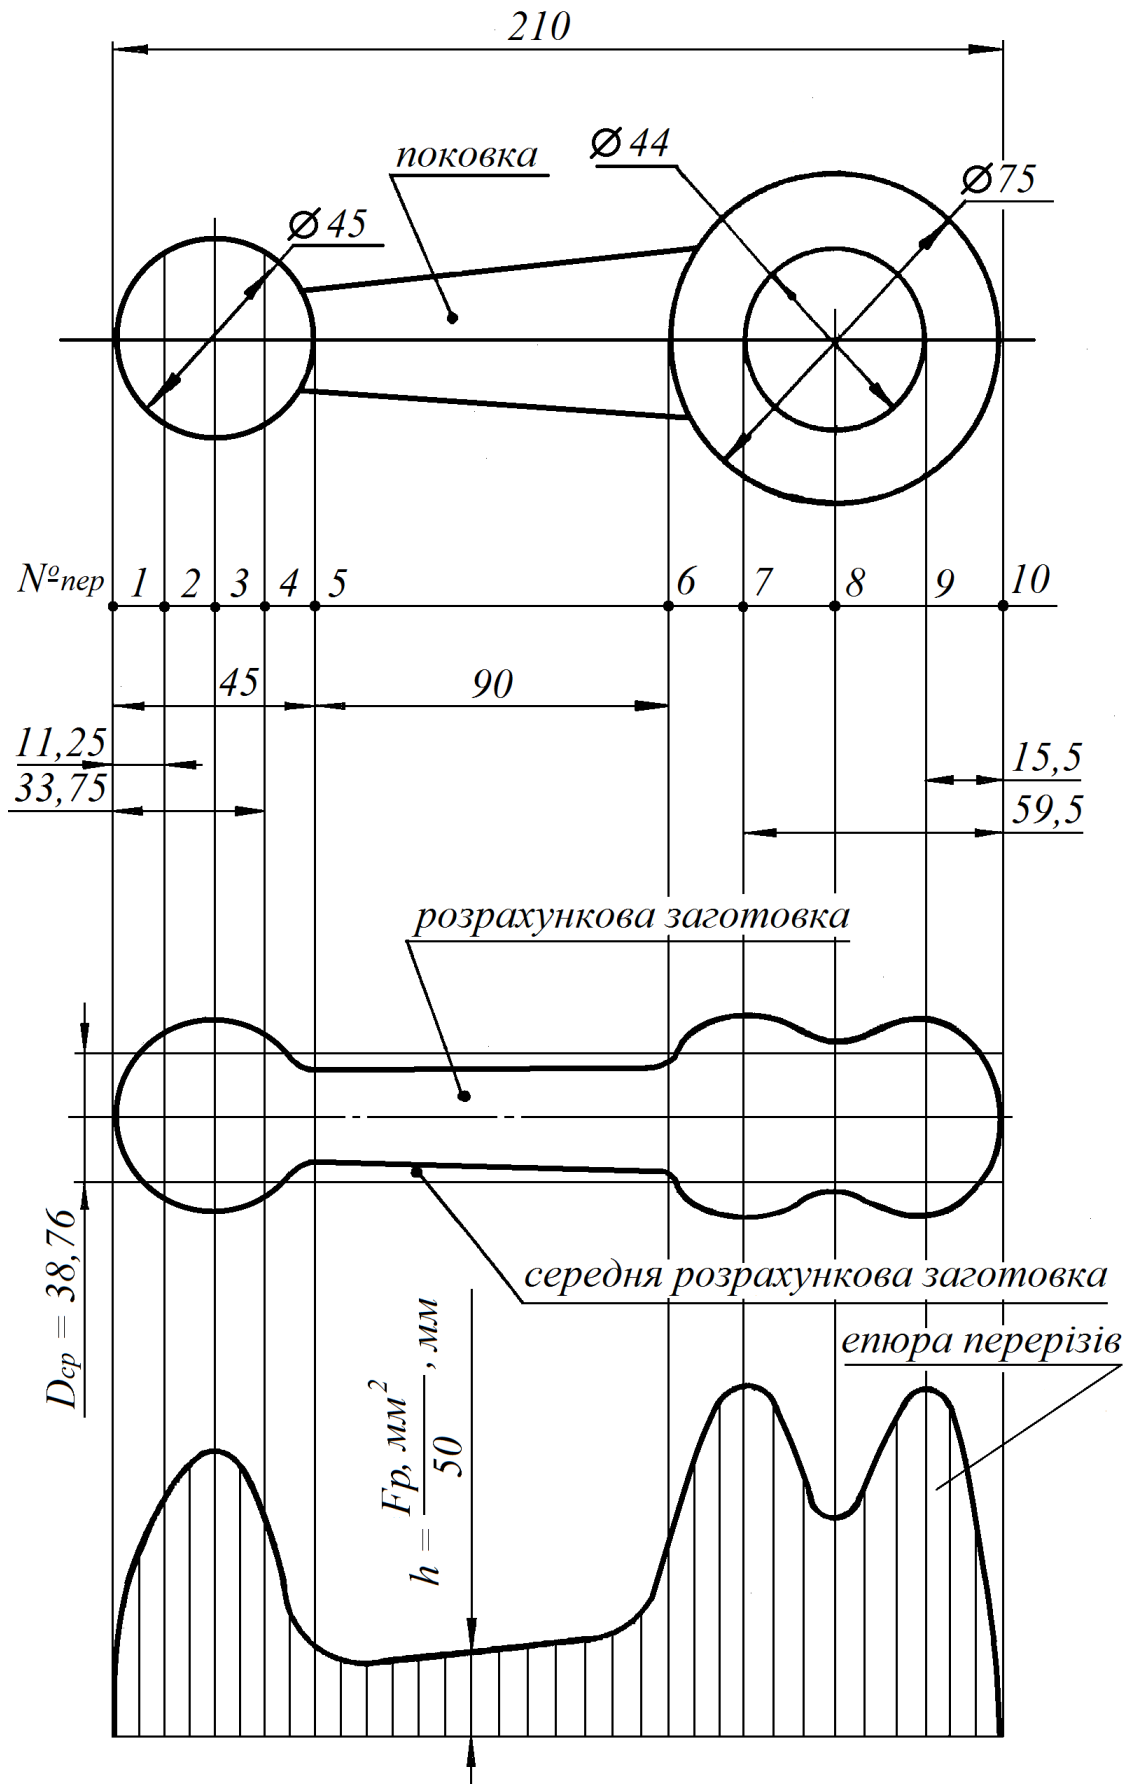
Елементарна розрахункова заготовка та епюри її перерізів
